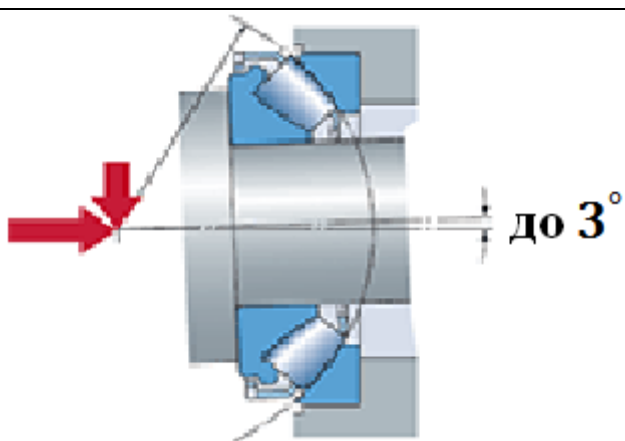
Упорный сферический роликовый подшипник. Источник: <http://www.bergab.ru>
